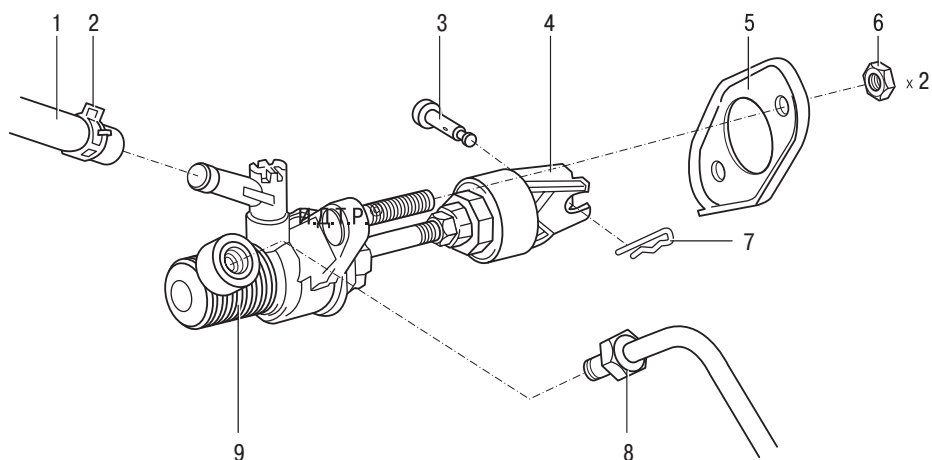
Главный цилиндр сцепления: 1 – патрубок главного цилиндра сцепления; 2 – хомут; 3 – фиксатор; 4 – вилка штока главного цилиндра сцепления; 5 – кронштейн; 6 – гайка; 7 – штифт вилки штока главного цилиндра сцепления; 8 – трубопровод привода сцепления; 9 – главный цилиндр сцепления
